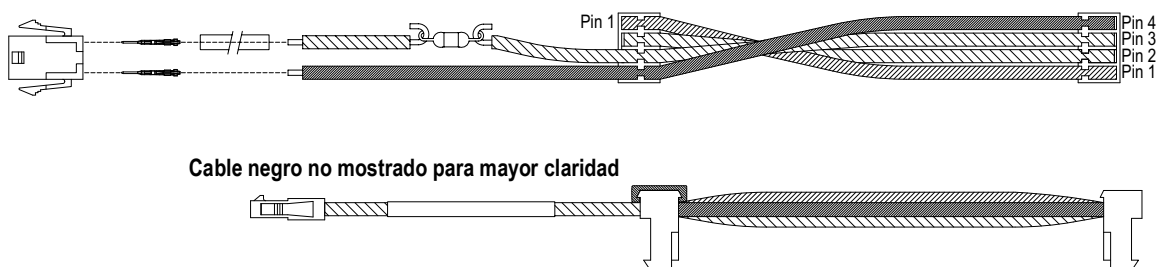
Mazo de cables retroadaptado para pantalla con retroiluminación LED y placa de CPU verde
